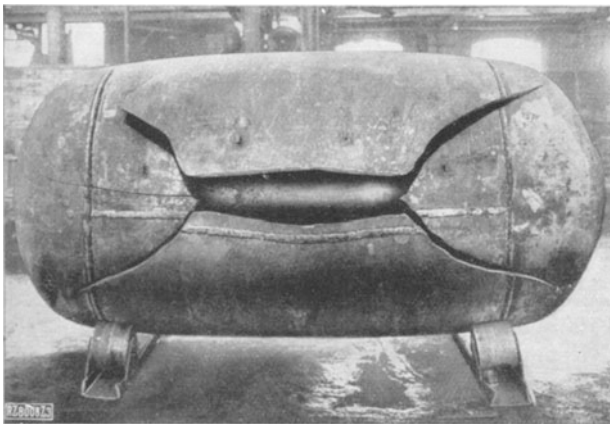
Versuchsdruckkessel, nach dem Pintschverfahren geschweißt, gerissen bei 155 at.
